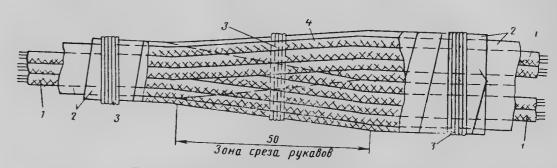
Ответвление гибких рукавов: 1— провод; 2— экранирующий рукав; 3— бандаж из ниток «Маккей»; 4— изоляционная лента
